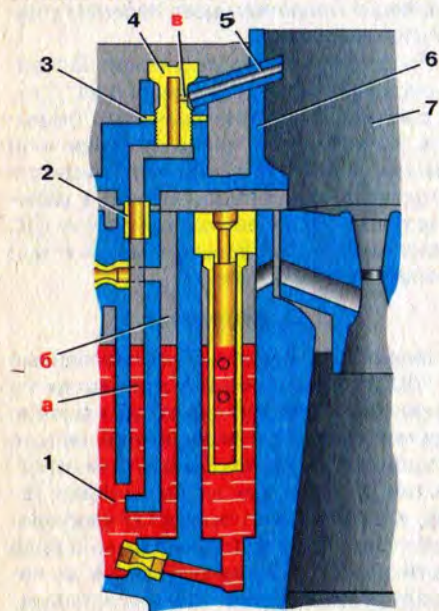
Схема эконостата: 1 - поплавковая камера; 2 - переходная втулка; 3 - уплотнительная прокладка; 4 - топливоподающий винт; 5 - распылитель; 6 - крышка карбюратора; 7 - главный воздушный канал; 8 - балансировочный канал поплавковой камеры; 9 - калиброванное отверстие топливоподающего винта
